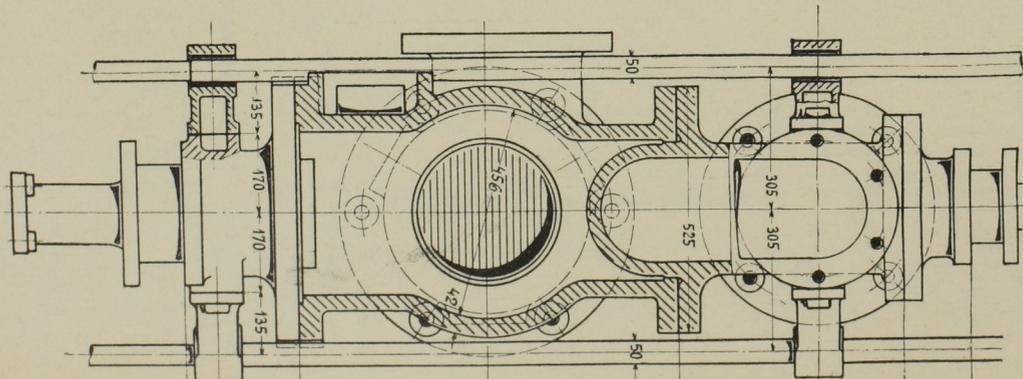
Grundriss der Pumpe. Masst. 1:15.
